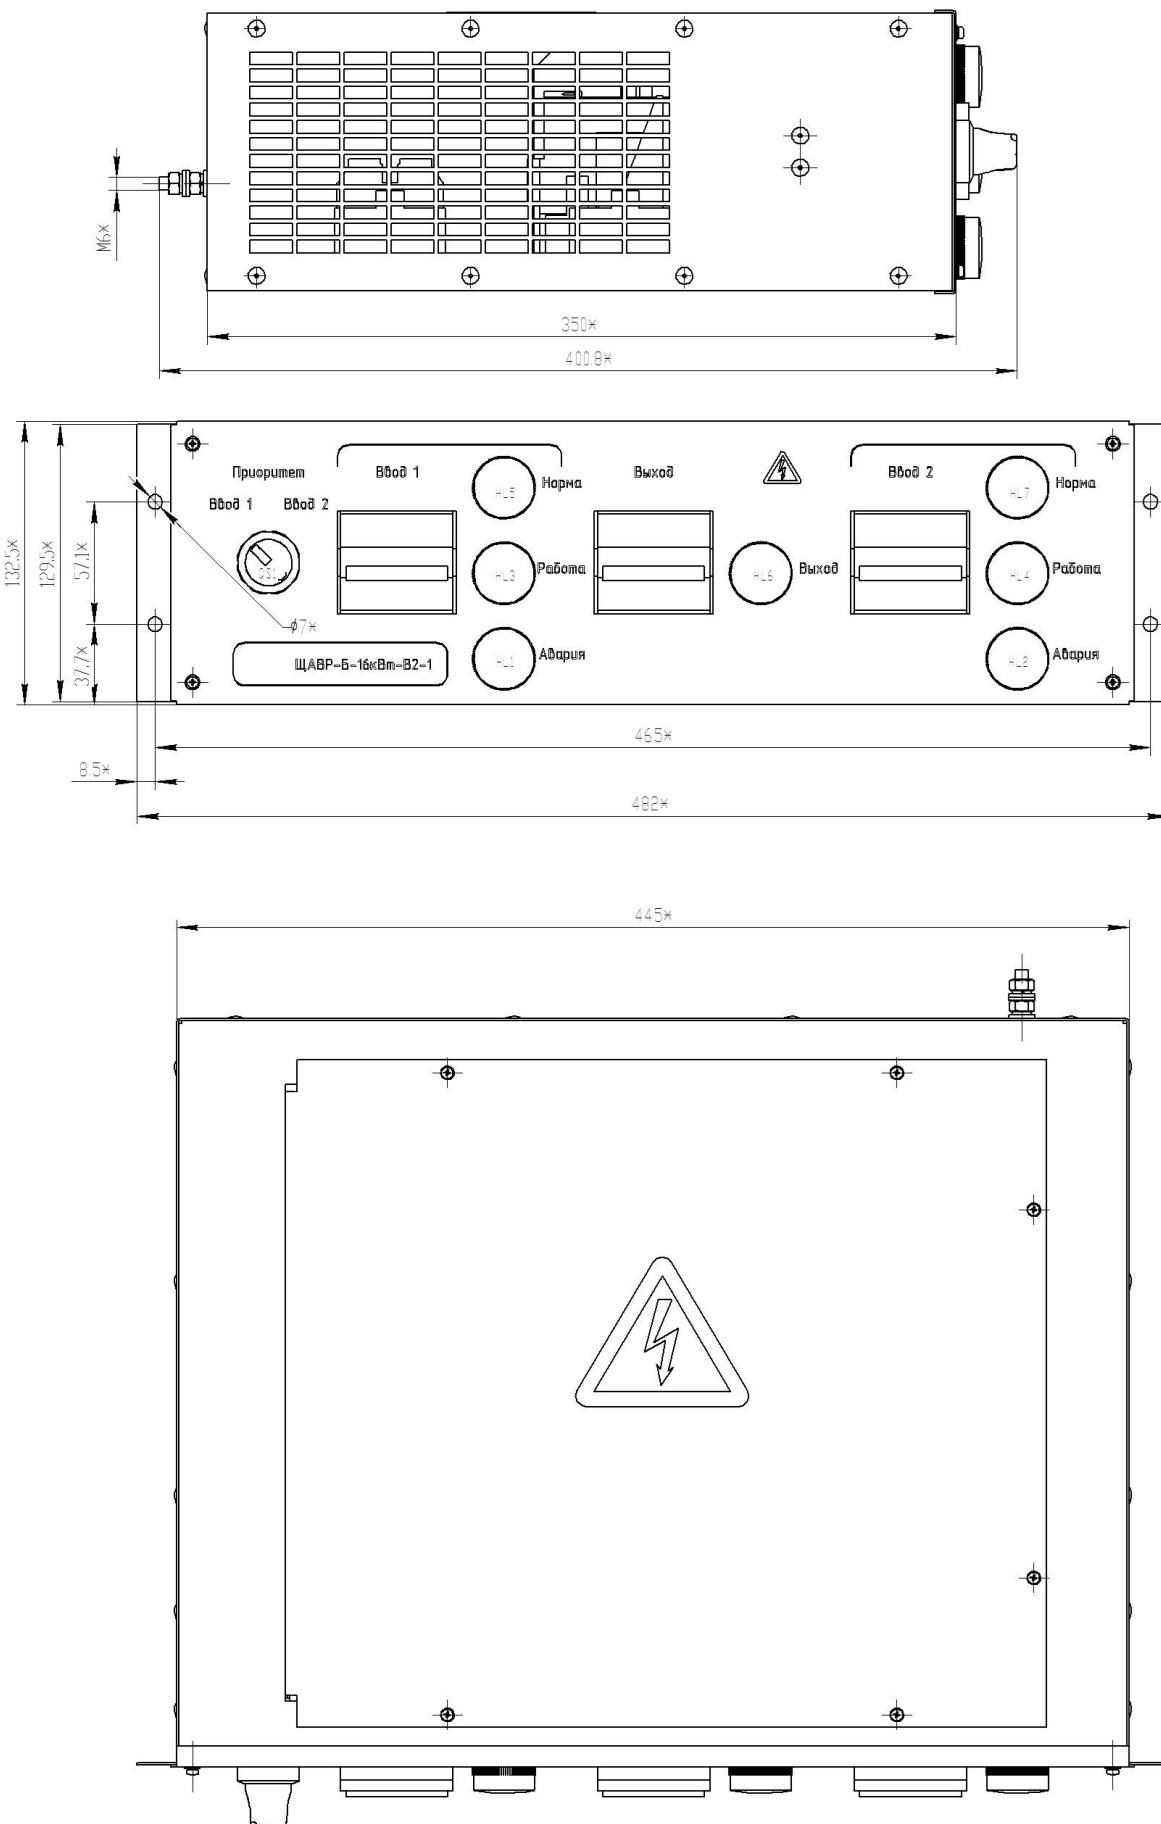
Габаритно-присоединительные размеры щита автоматического включения резерва ШzAVP-Б-8кВт-В2-2.
